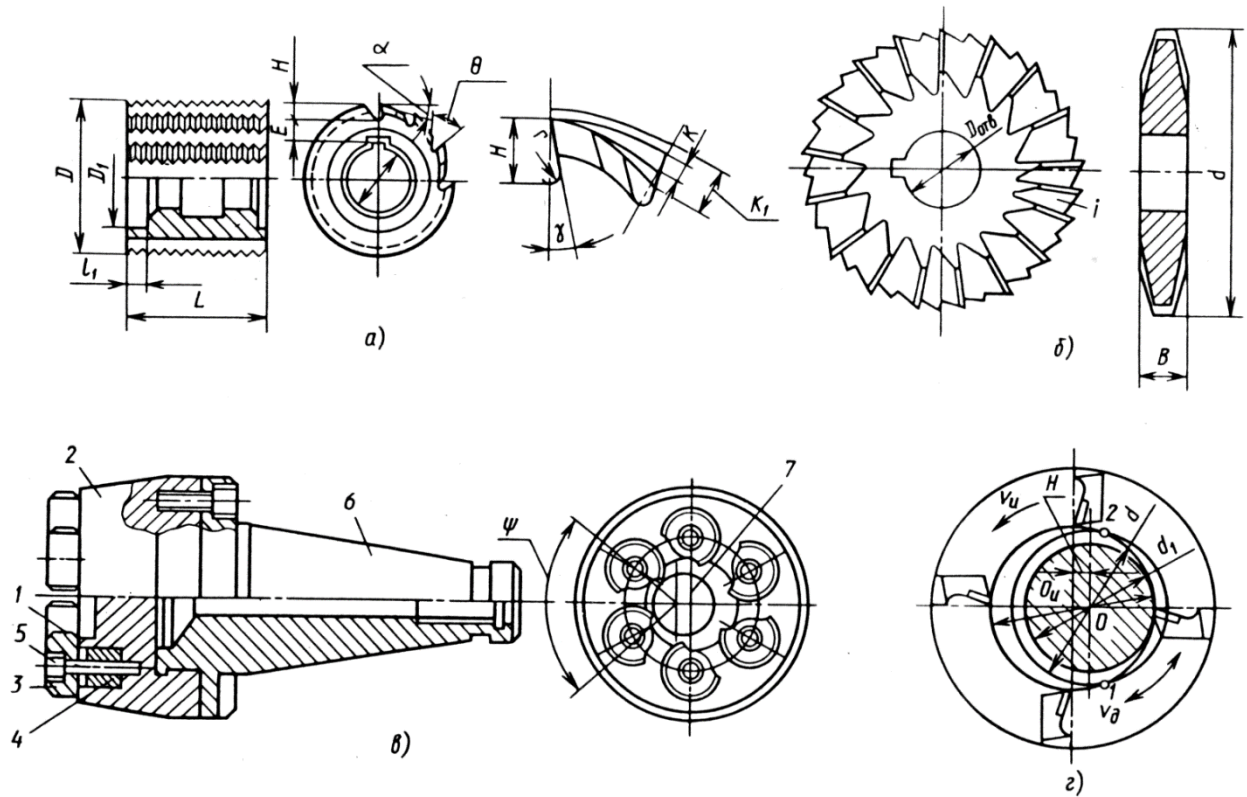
Різьбові фрези: а – гребінчасті циліндричні; б – дискові; в – складені гребінчасті охоплюючі: 1 – гребінки; 2 – корпус; 3 – зірки; 4 – втулка; 5 – гвинт; 6 – конічний хвостовик; ψ – кут контакту зубців фрези із заготовкою
